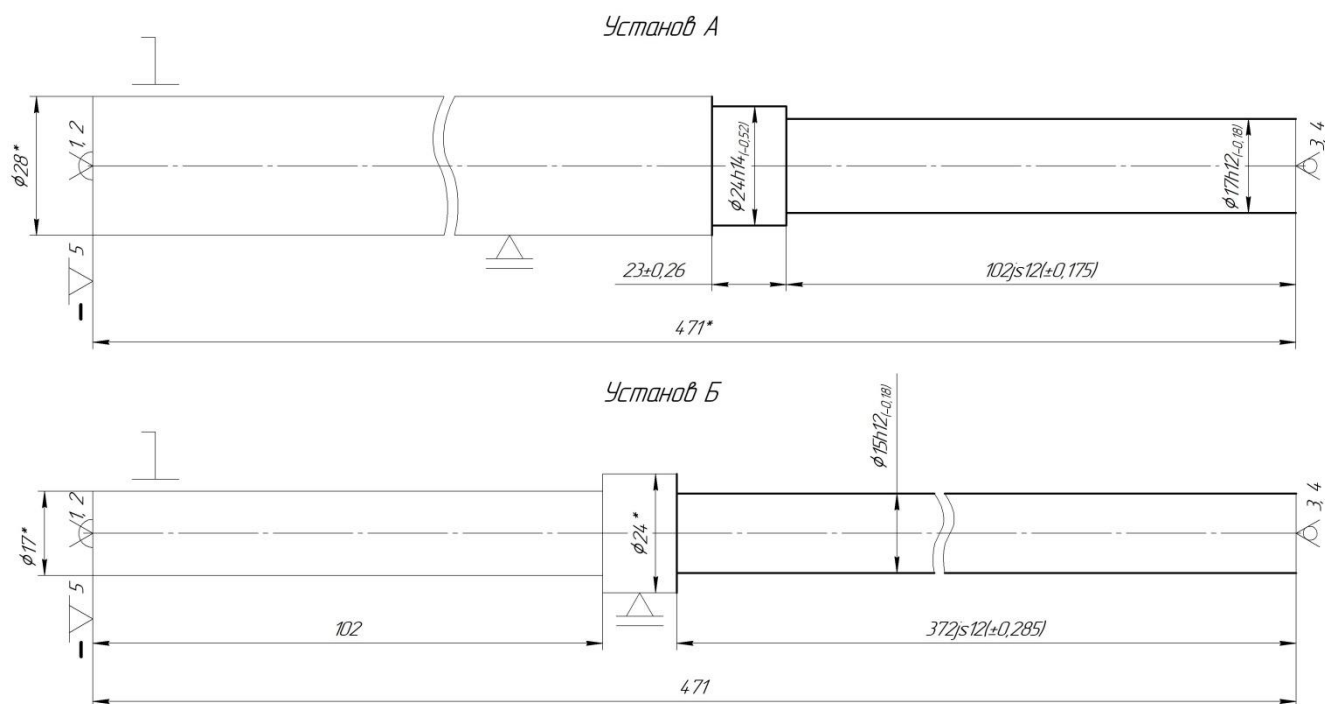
Схема базування деталі із плаваючим центром
